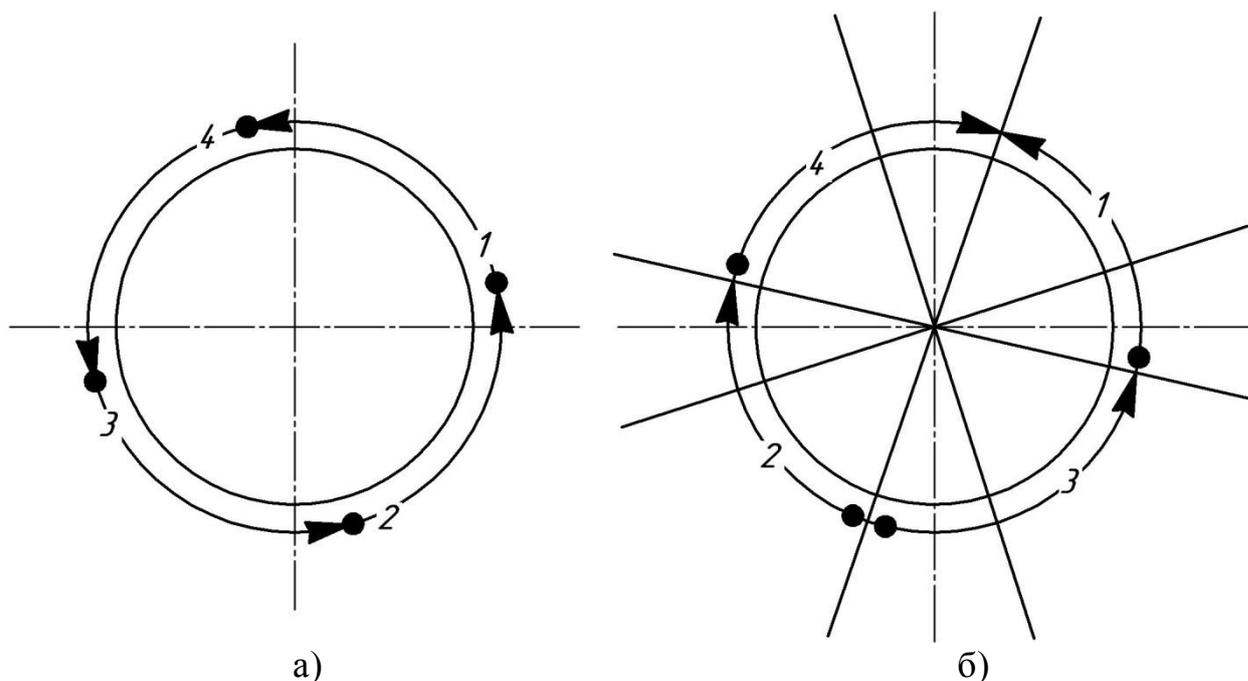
Порядок сварки участков корневого слоя шва при сварке горизонтального (а) и вертикального (б) стыка труб одним сварщиком
